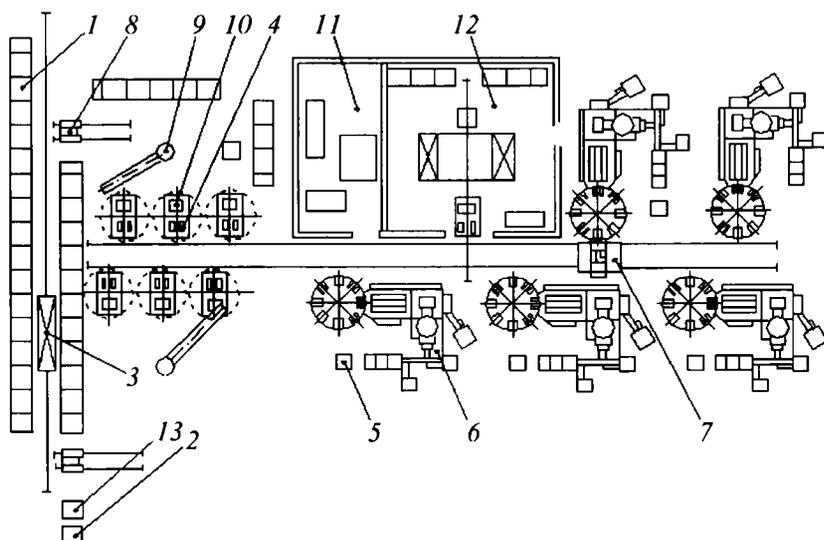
ГАУ с АТСС линейного типа, с поперечным расположением оборудования и рельсовой транспортной тележкой:
